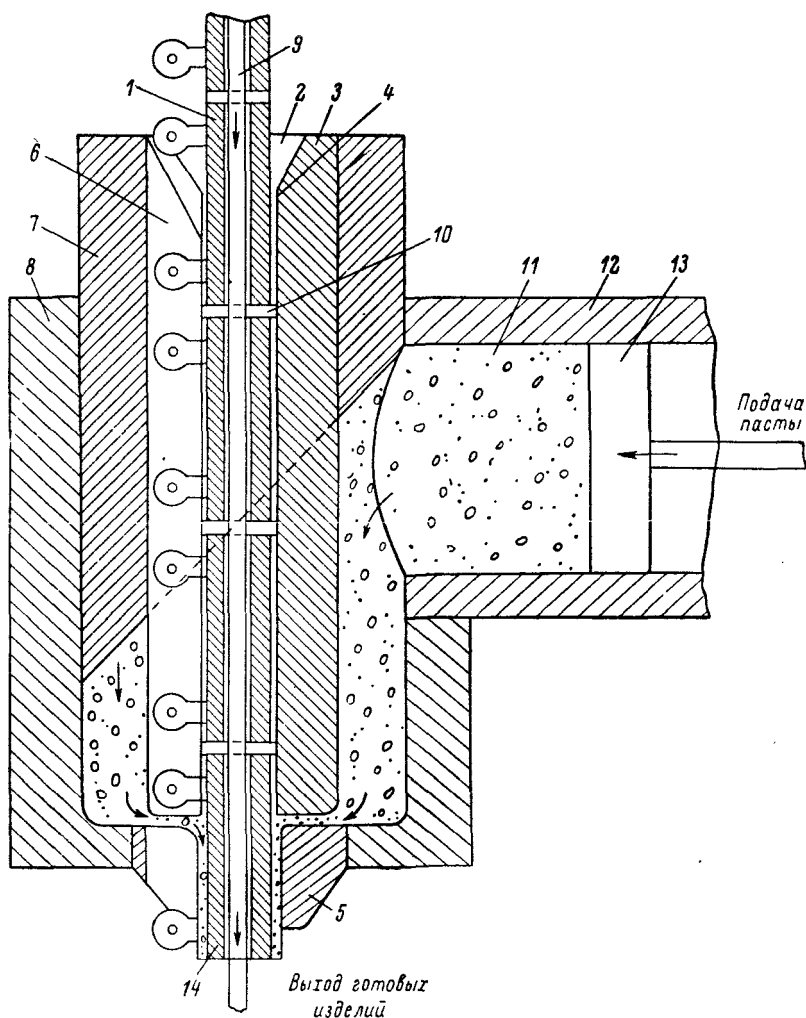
Прибор для опрессовки резисторов ПТ пастой.
